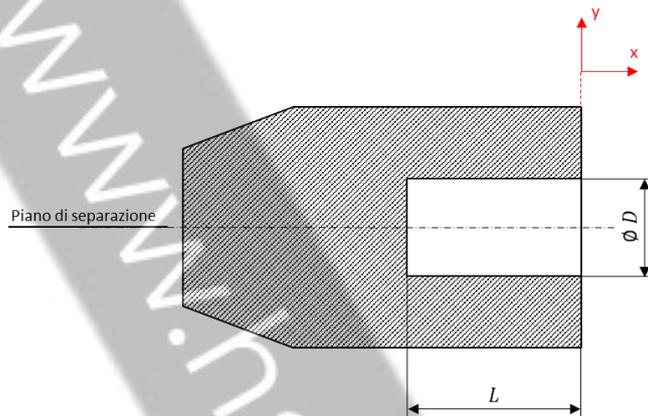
Sezione di un componente da realizzare con un processo di fonderia
